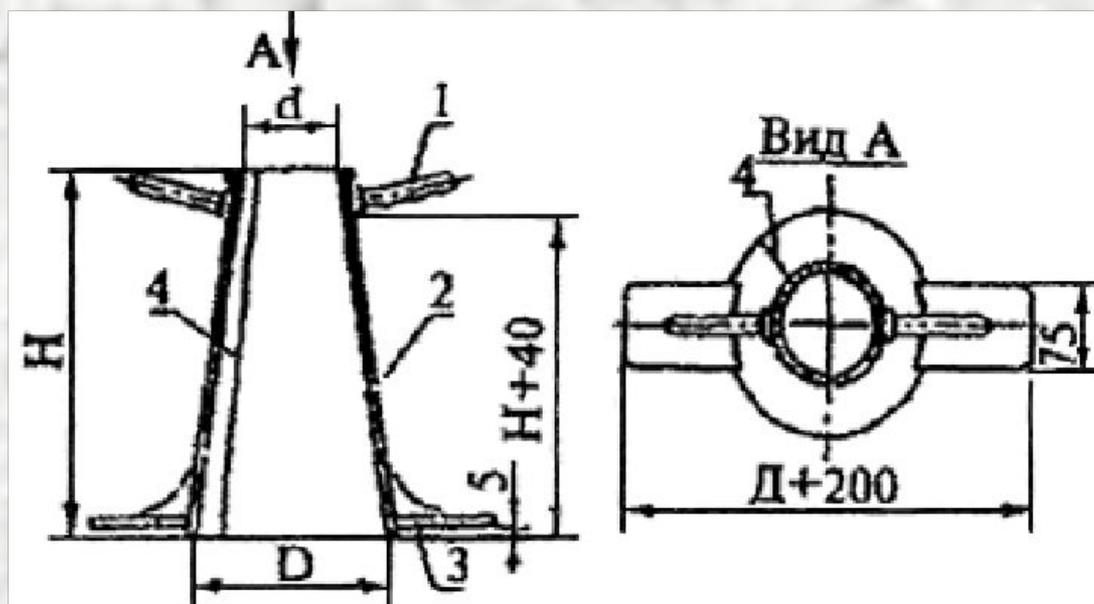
Стандартный конус для испытаний: 1 - ручки, 2 - корпус из листовой стали толщиной не менее 1.5 мм, 3 - упоры для ног, 4 - сварной шов.
